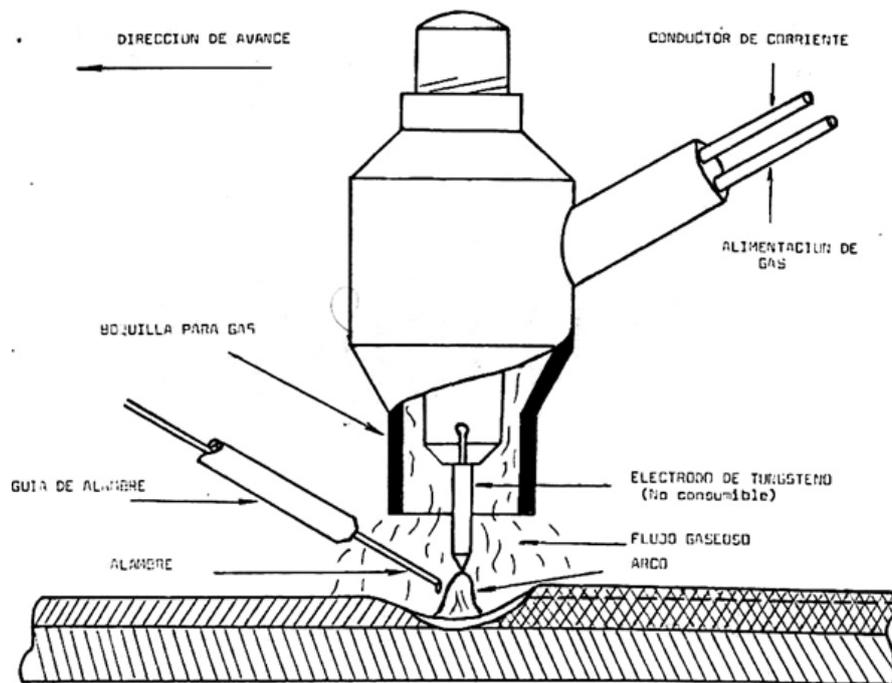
Soldadura por arco de tungsteno y protección gaseosa – Fuente: <http://www.histarmar.com.ar/Astilleros/Diccionario/LetraS.htm>
